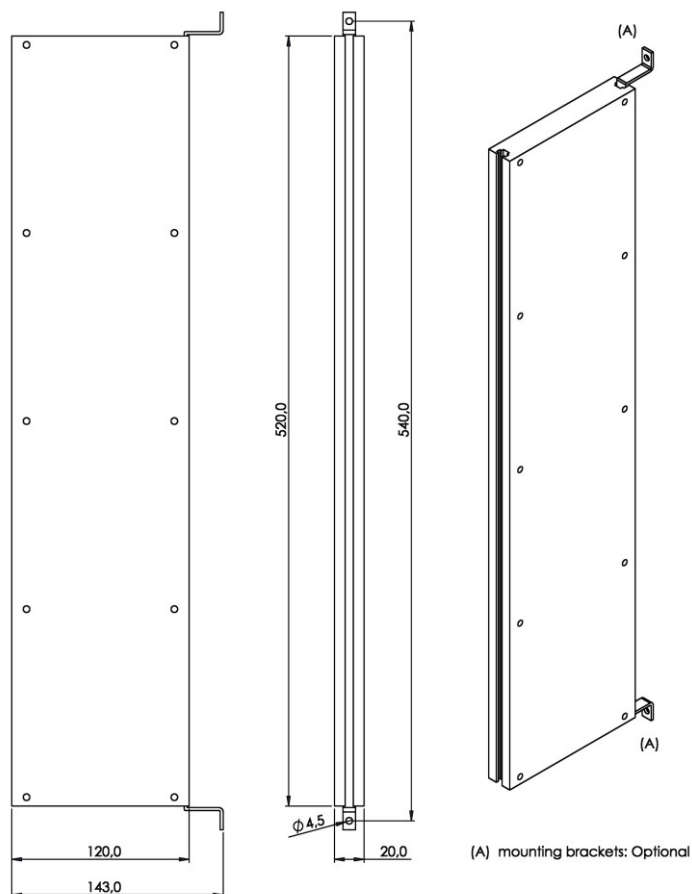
Dimensioni resistenza di frenatura UL / UL braking resistor dimensions
